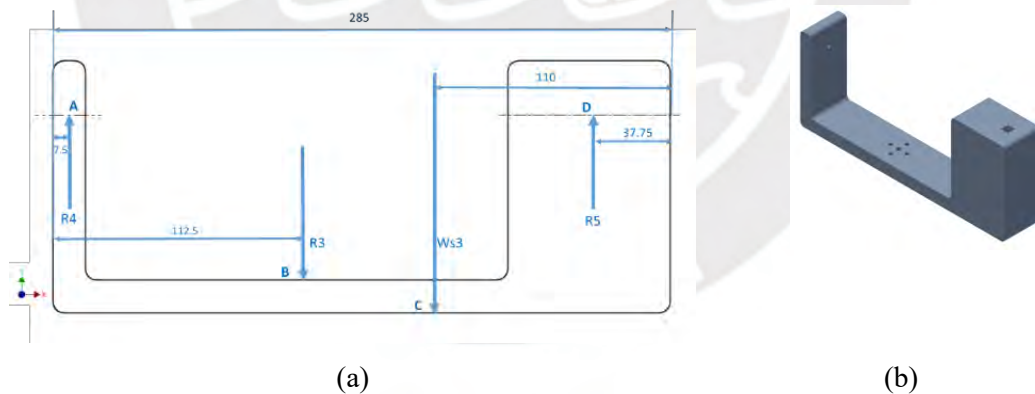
Soporte de flexión/extensión (a) DCL, (b) Vista 3D isométrico
